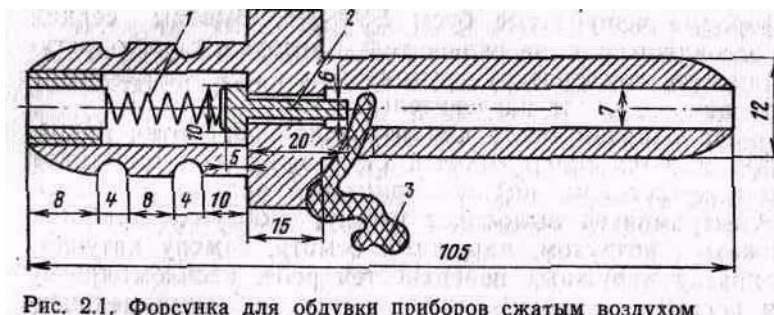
Форсунка для обдувки приборов сжатым воздухом
